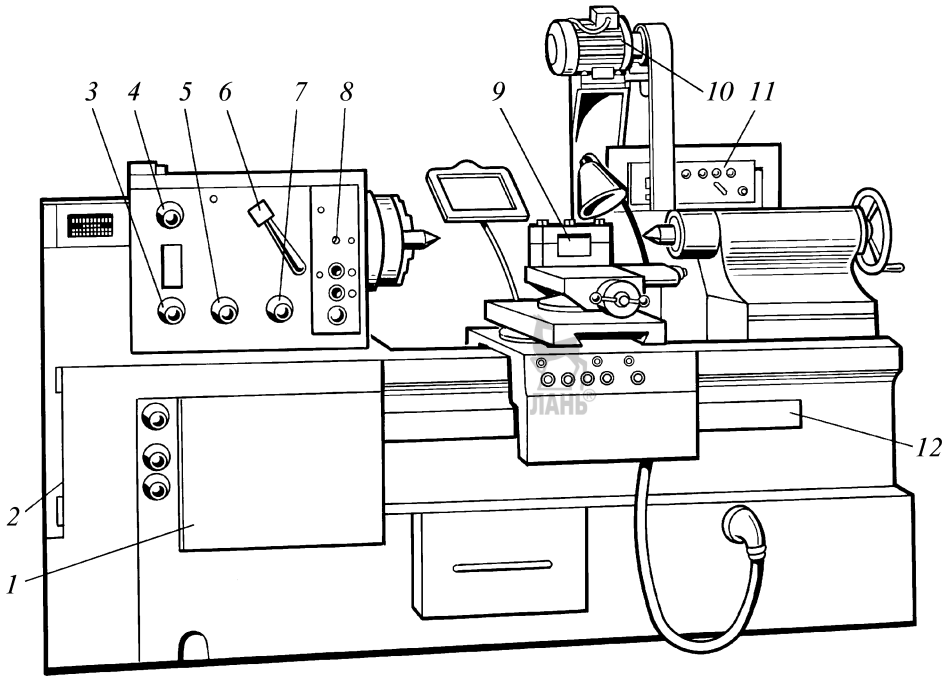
Универсальный токарно-затыловочный станок 1E811:
